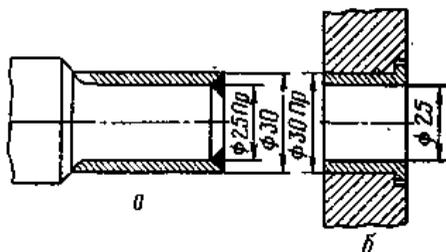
Схема установки ремонтной втулки: а – на концевую шейку вала;
